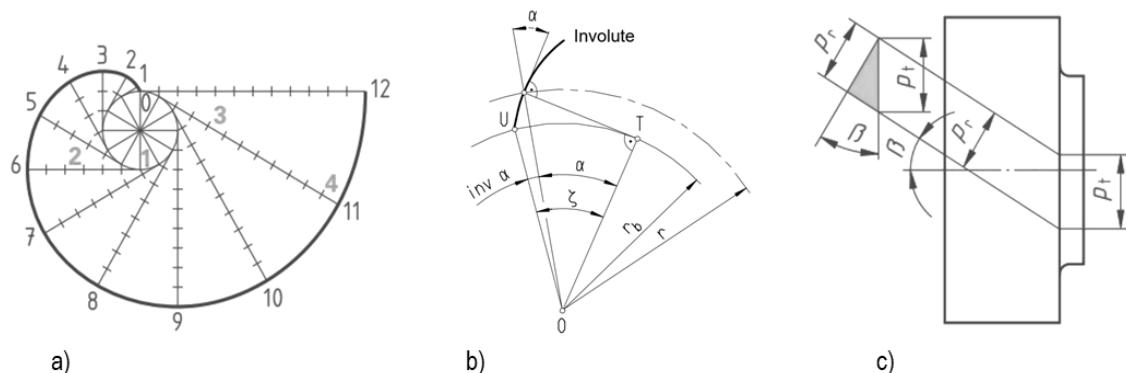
a),b) Definition Evolente / Involute c) Schrägverzahnung / helical gear
